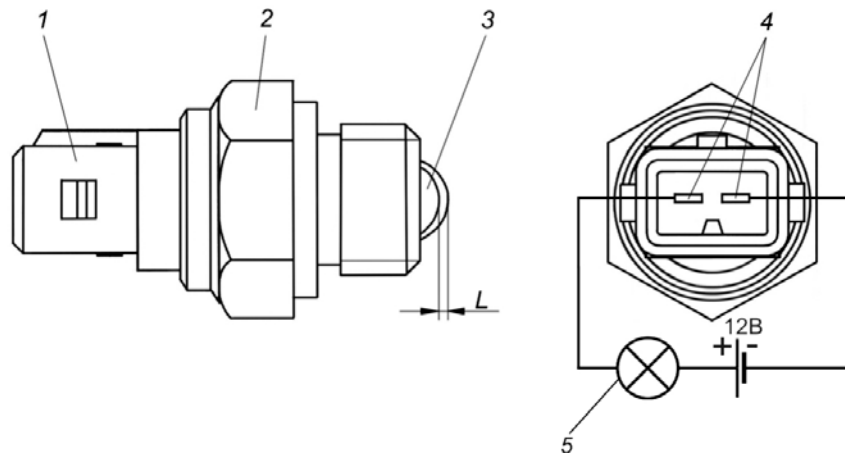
Выключатель света заднего хода: 1 - герметичная колодка; 2 - корпус; 3 - шарик; 4 – выводы; 5 - лампа
